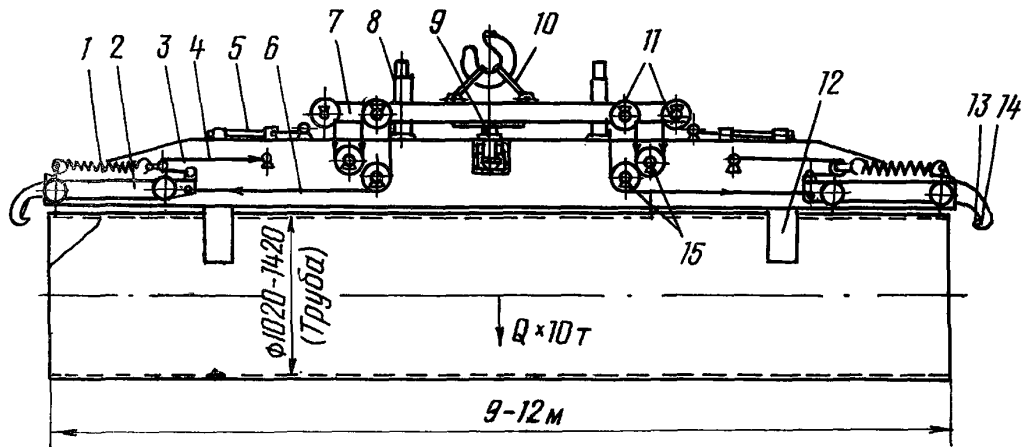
Конструктивная схема захвата трубного автоматического ЗТА-102:
